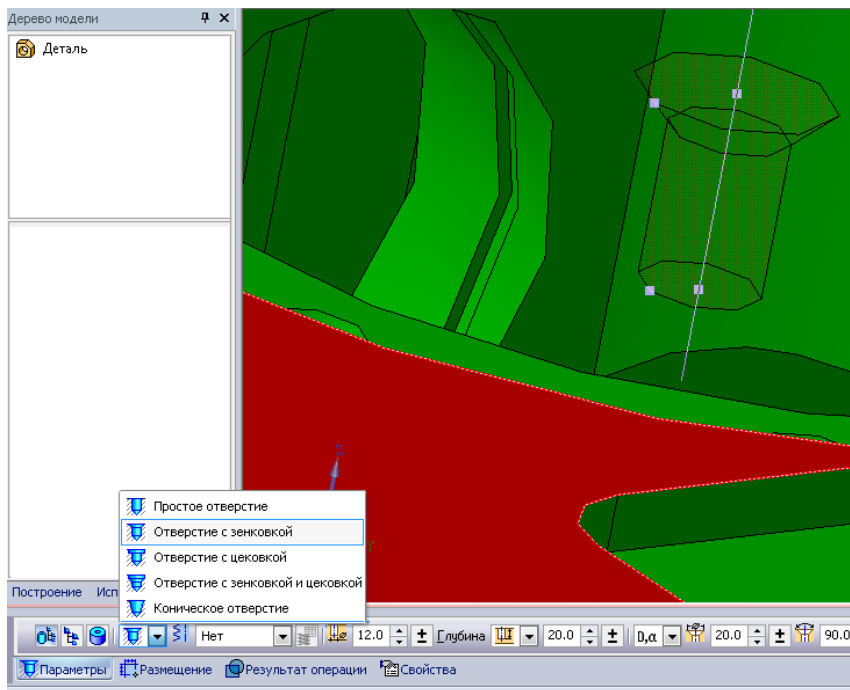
Побудова отвору в деталі Корпус механізму повороту
